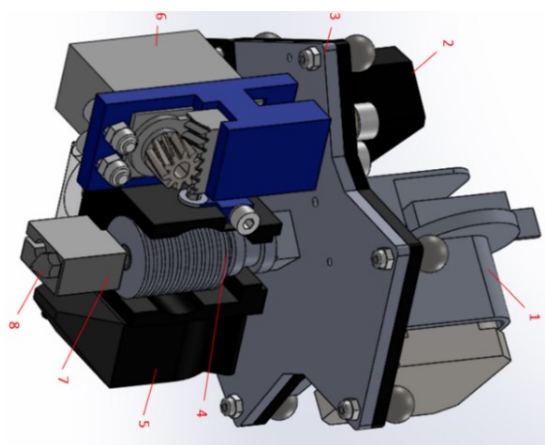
Модернизированная печатающая головка для принтера EPIT 5.1 Carbon: 1 – экструдер подачи филамента; 2 – электро-контакт подключения головки; 3 – площадка печатающей головки; 4 – радиатор охлаждения филамента; 5 – вентилятор охлаждения расплава; 6 – механизм обрезки филамента; 7 – блок нагрева филамента; 8 – сопло
